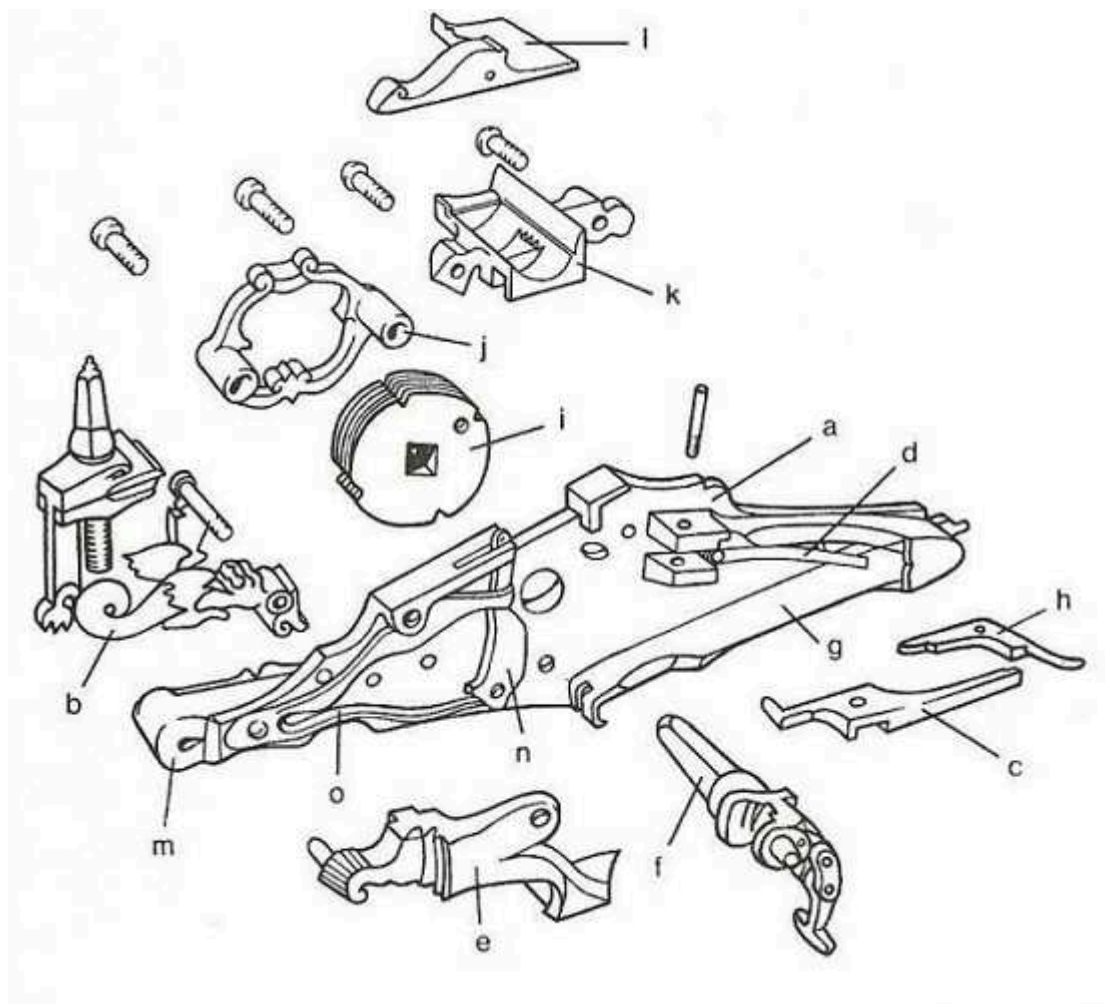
Těšínská detail zámku [<http://www.lovuzdar.sk>]
